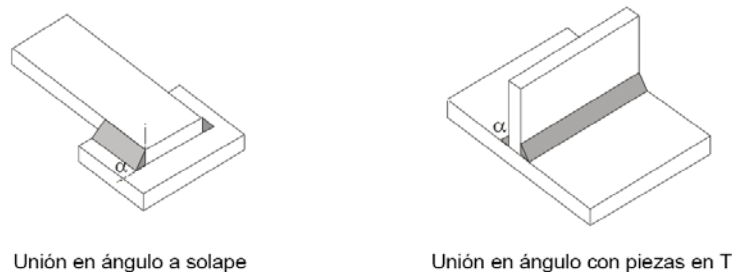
UNIONES SOLDADAS EN ÁNGULO CONTINUAS
